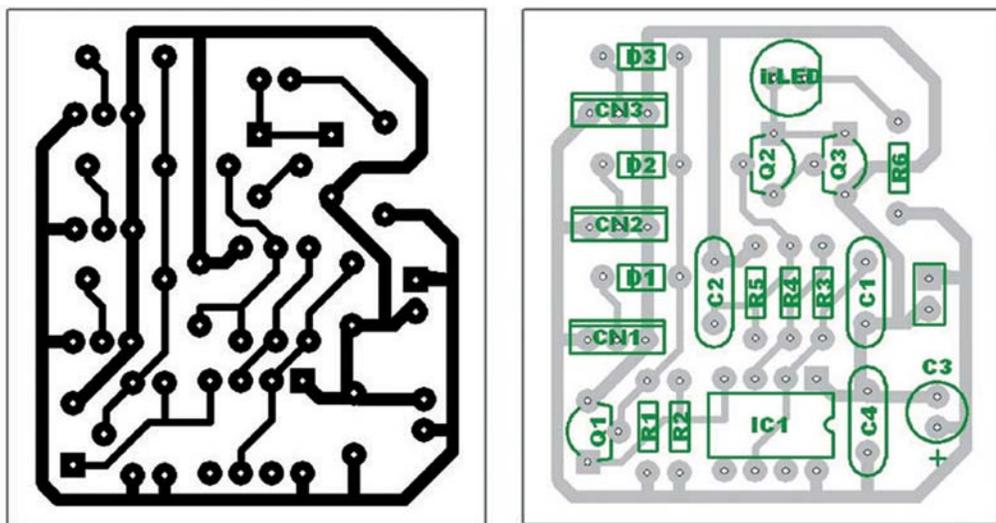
Circuito impreso. A: Lado de las soldaduras. B: lado de los componentes
